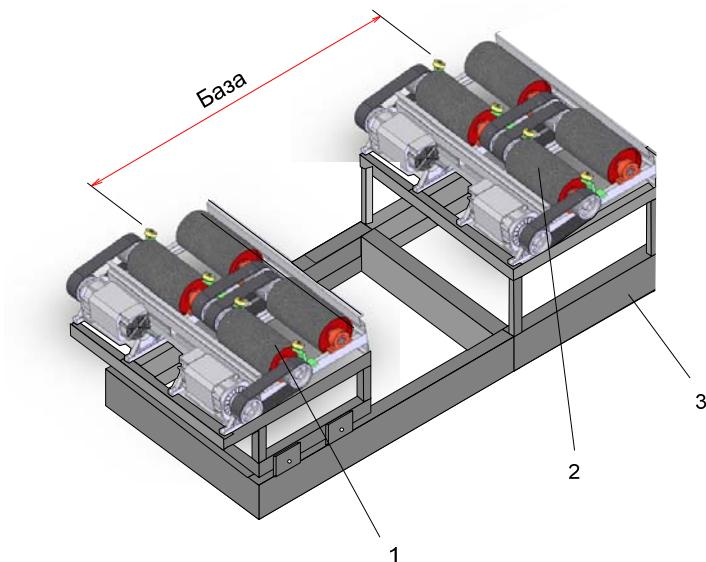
Универсальный роликовый стенд с изменяемой базой для испытания полноприводных автомобилей: 1 – подвижный блок роликов; 2 – неподвижный блок роликов; 3 – рама
